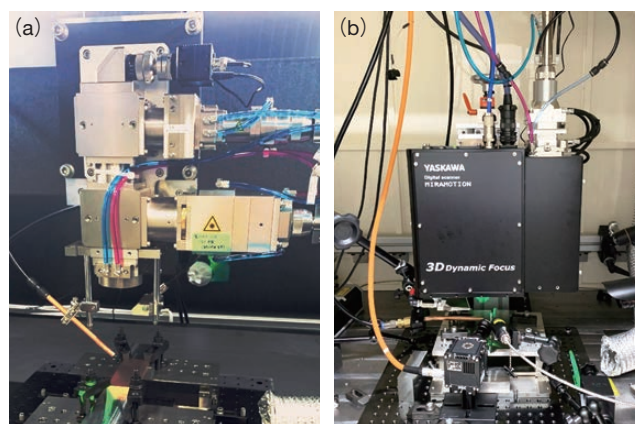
レーザ溶接加工時の加工光学系外観 (a)光学ヘッド(レーザックス製), (b)ガルバノスキャナ(安川電機製)との組み合わせ
